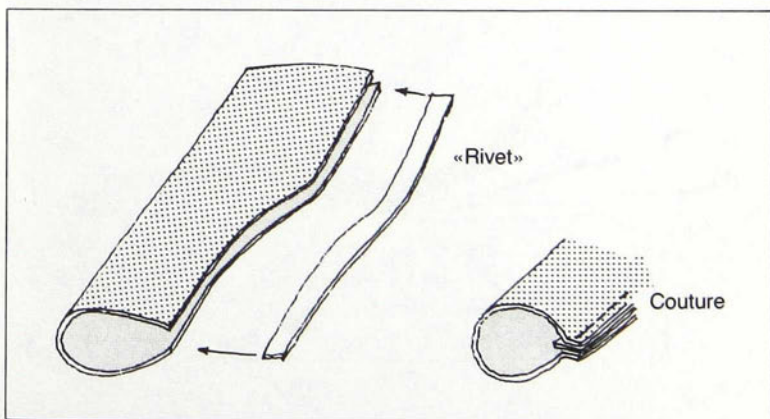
En reliant les deux extrémités de la jambe, le cordonnier ajoute un «rivet» ou passepoil entre les deux, avant de coudre les trois épaisseurs.
